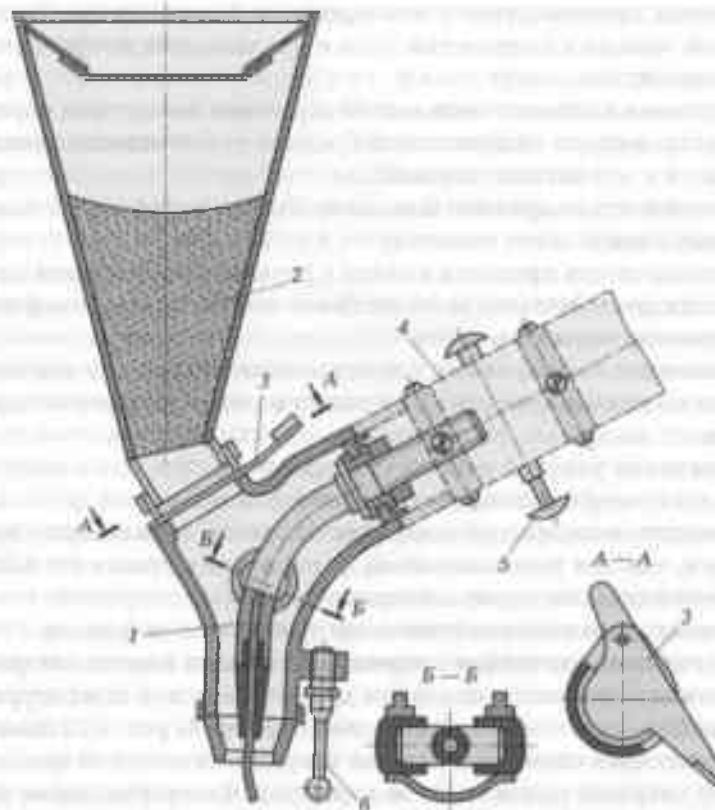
Полуавтоматическая сварка и наплавка под слоем флюса:
